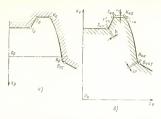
Сравнение рабочего профиля (а) инструмен тальной рейки и теоретического профиля (б) основного червяка червячной шлицевой фрезы
